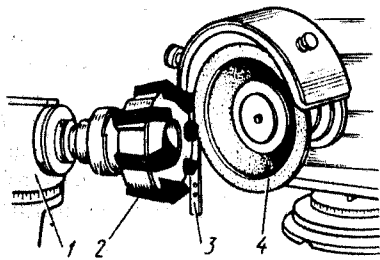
Заточка торцовой фрезы алмазным кругом:
